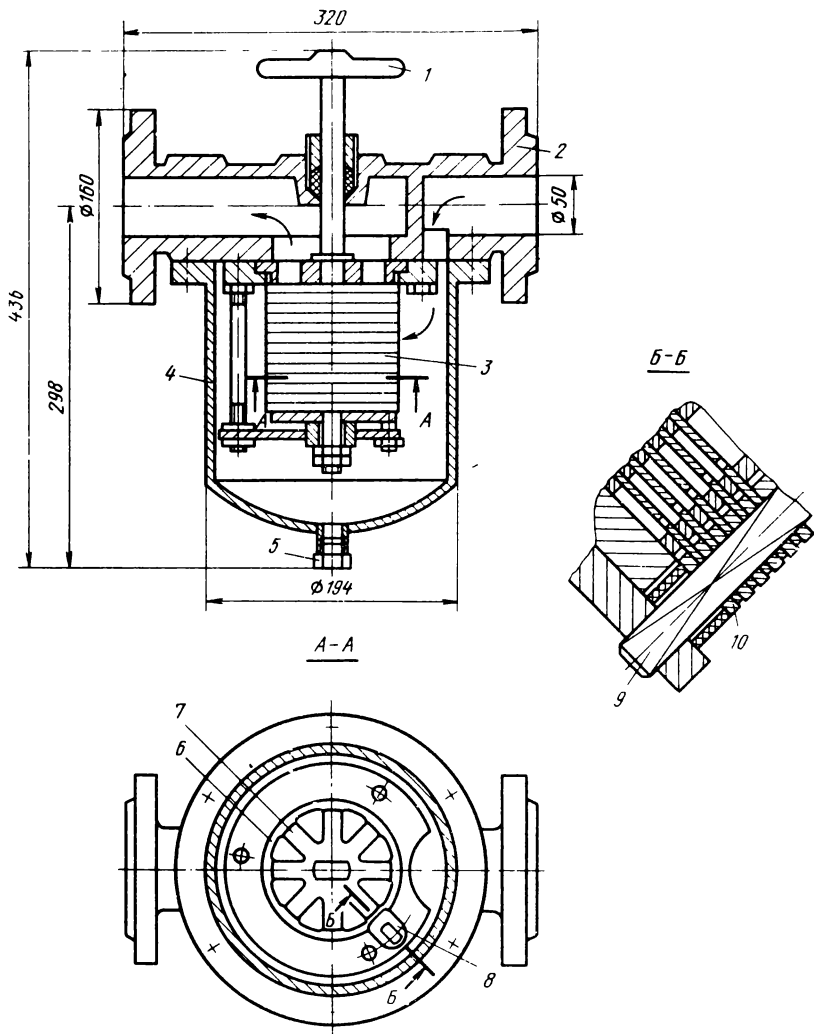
Дискный фильтр жидкой смазки ФДЖ-50
